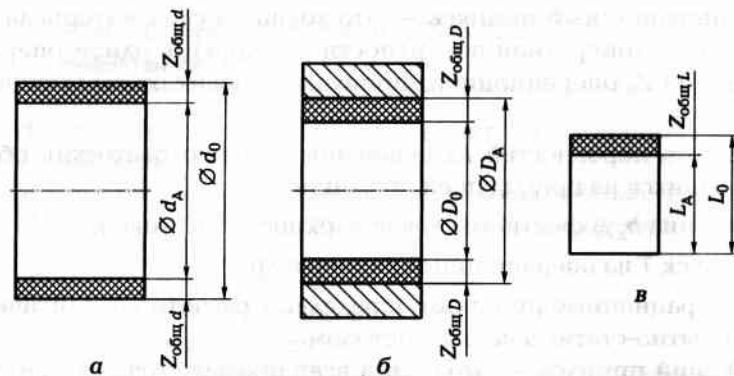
Схема расположения припусков на механическую обработку: а — для наружной цилиндрической поверхности; б — для внутренней цилиндрической поверхности; в — для плоской поверхности
